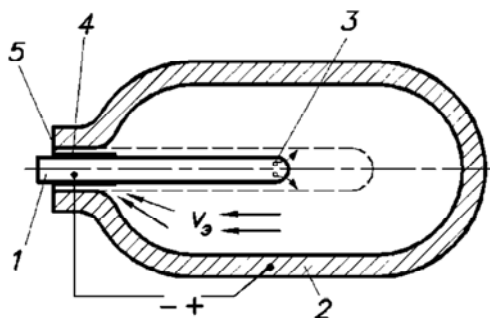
Схема обработки внутренней полости в заготовках, изготовленных из трудно деформируемых сплавов:
